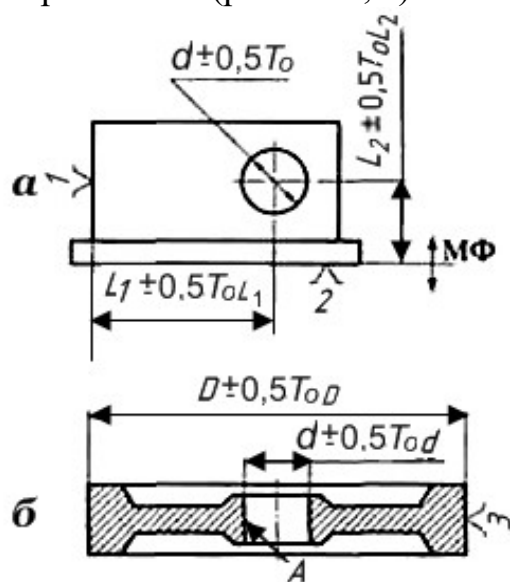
Позиционный допуск: а – оси диаметра отверстия относительно баз механической обработки; б – оси диаметра отверстия d относительно базового диаметра D ; $\pm 0,5 T_0$ – предельные отклонения размера; 1 , 2 , 3 – базы; A – внутренняя поверхность
